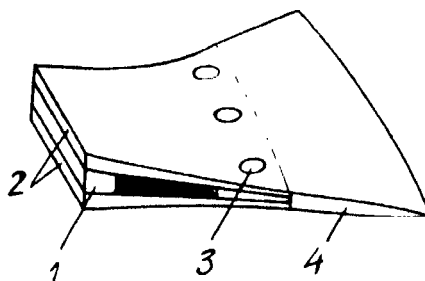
Fer de hache fabriqué par soudure
